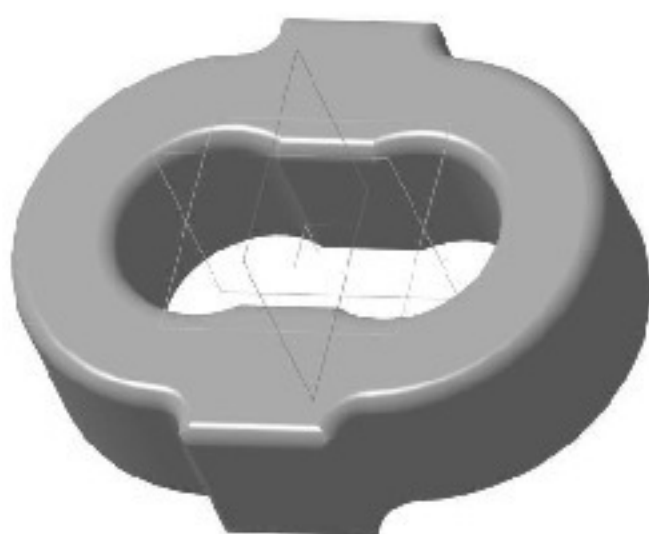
3D-модель заготовки при литті в оболонкові форми
